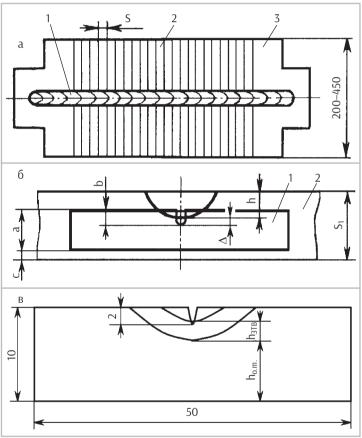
Валиковая проба с наплавкой (а), схема вырезки образцов для испытаний на ударный изгиб (б) и обозначение участков сварного соединения, которые входят в состав ударного образца (в): 1— наплавленный валик; 2— составные бруски; 3— выводная планка; $h_{\text{напл}}$ — участок с наплавленным металлом; $h_{\text{3ТВ}}$ — участок 3ТВ; $h_{\text{о.м.}}$ — участок основного металла.
